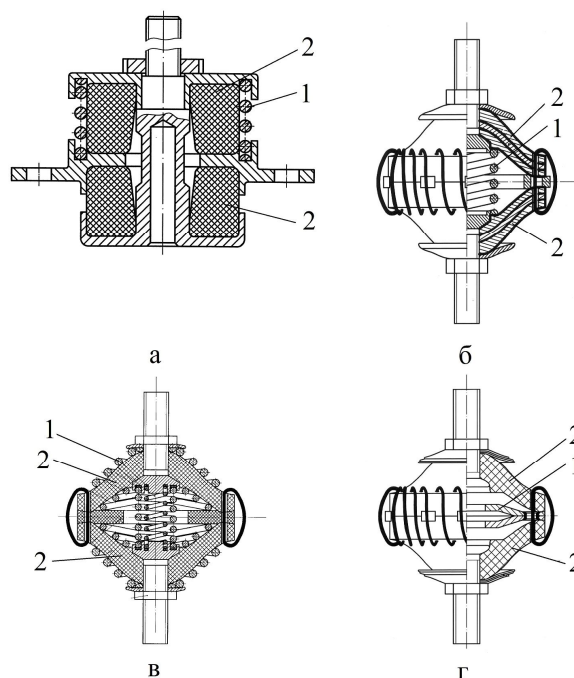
Конструкции виброизоляторов с пружинными разгрузочными и противоударными устройствами: 1 - разгрузочная пружина; 2 - УДЭ
